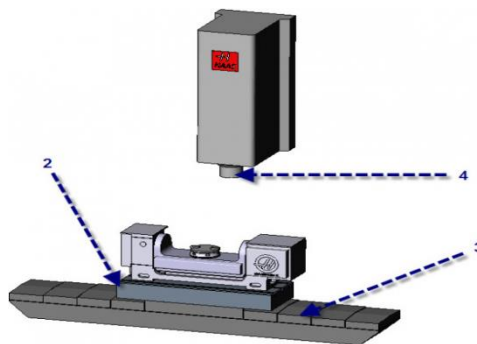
Будова фрезерного верстата з ЧПК
